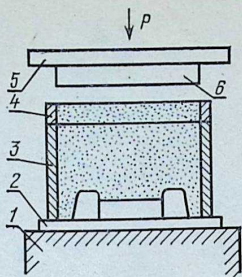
Схема формовочной машины с верхним уплотнением формовочной смеси:
